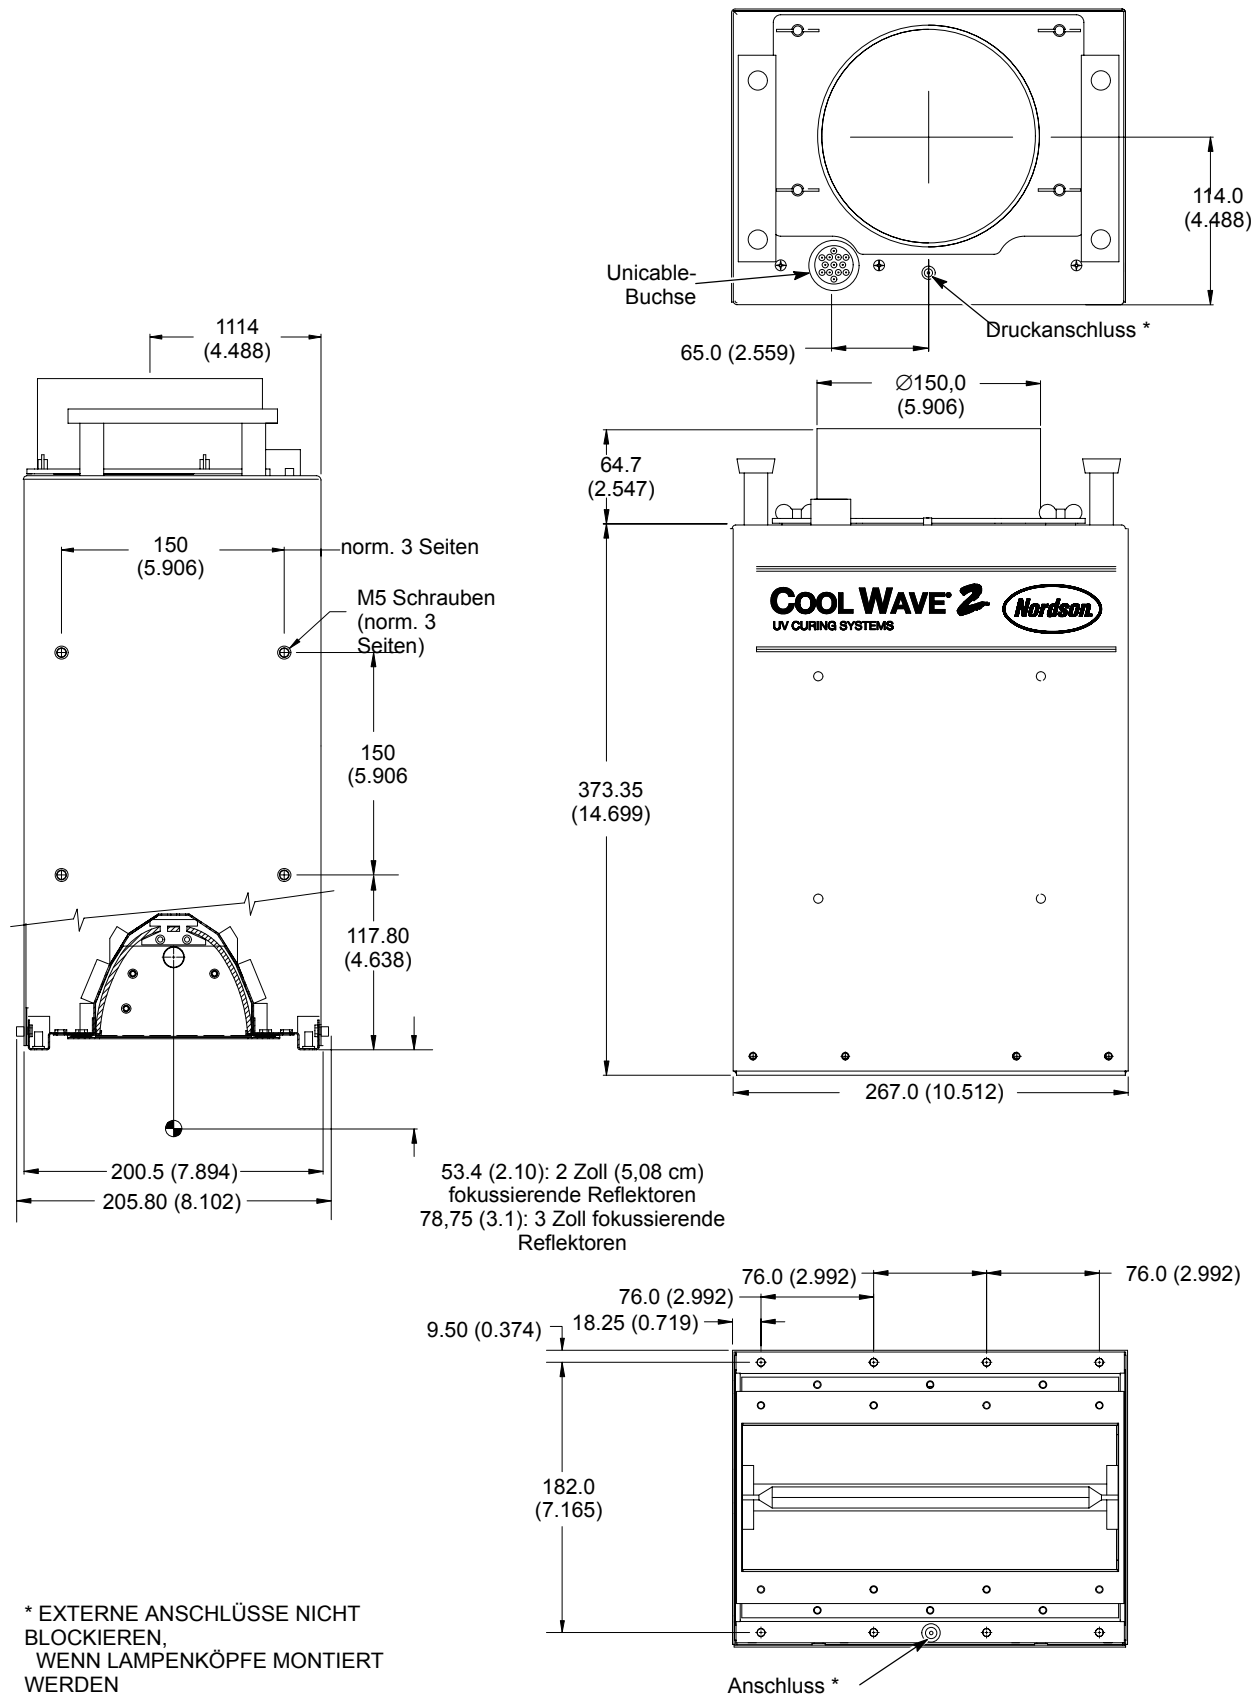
Maße, Lampenkopf mit externem Gebläse
